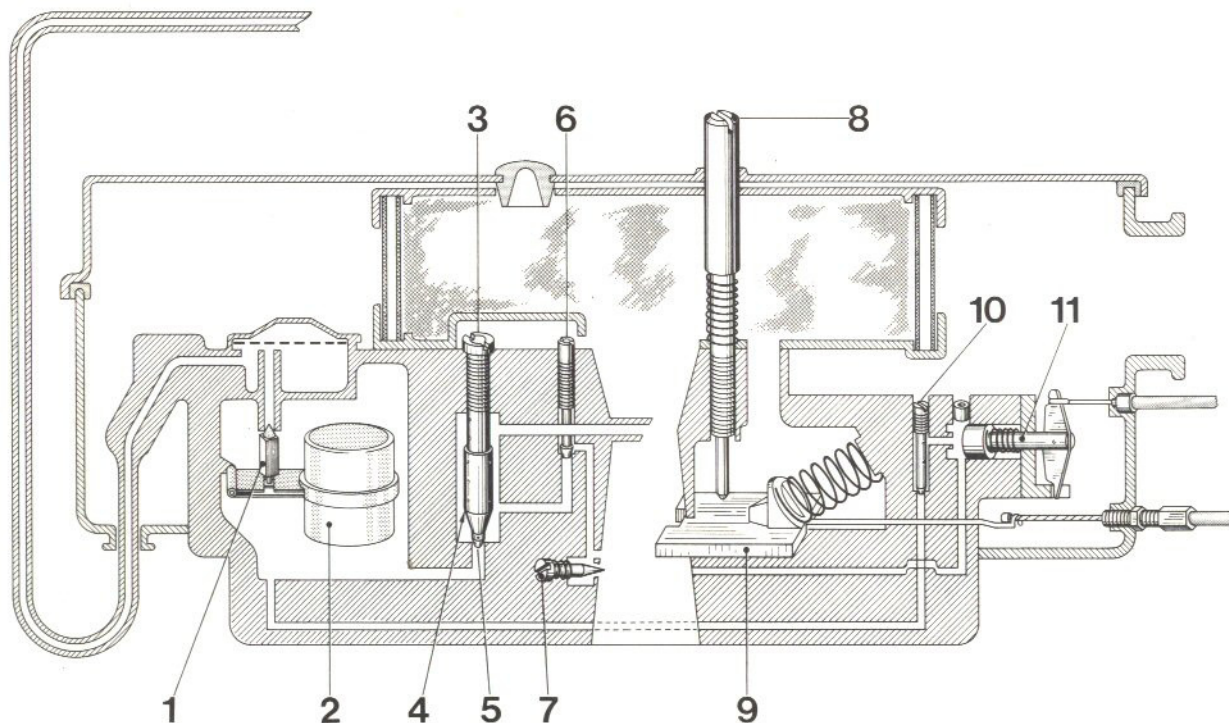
Carburatore tipo SI 20/20 D e SI 24/24 E.
